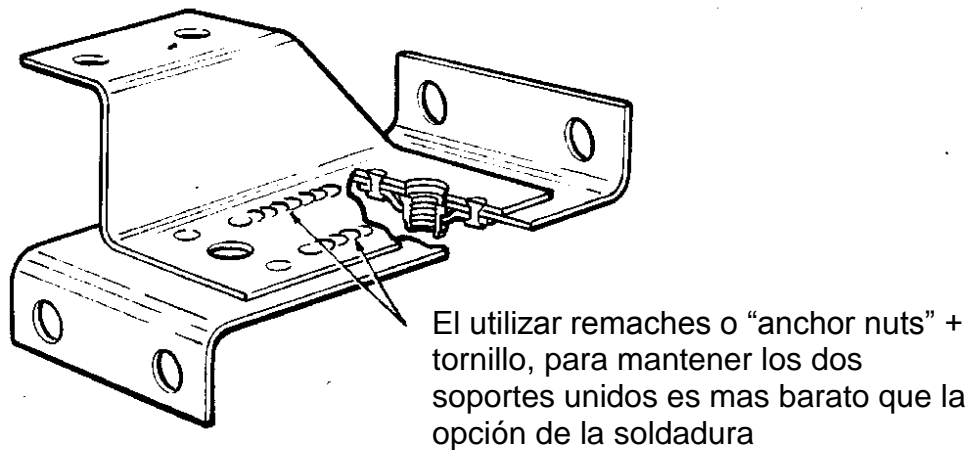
Evitar soldaduras con remaches o uniones atornilladas
